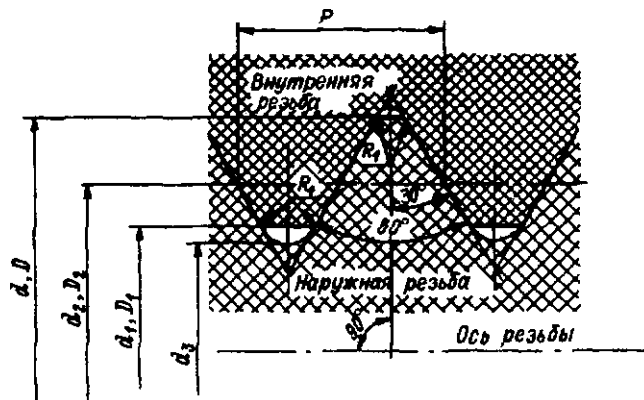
Профиль резьбы для деталей из пластмассы
